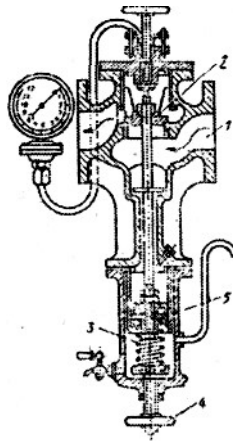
Редукційний клапан: 1 — канал; 2 — золотник;
